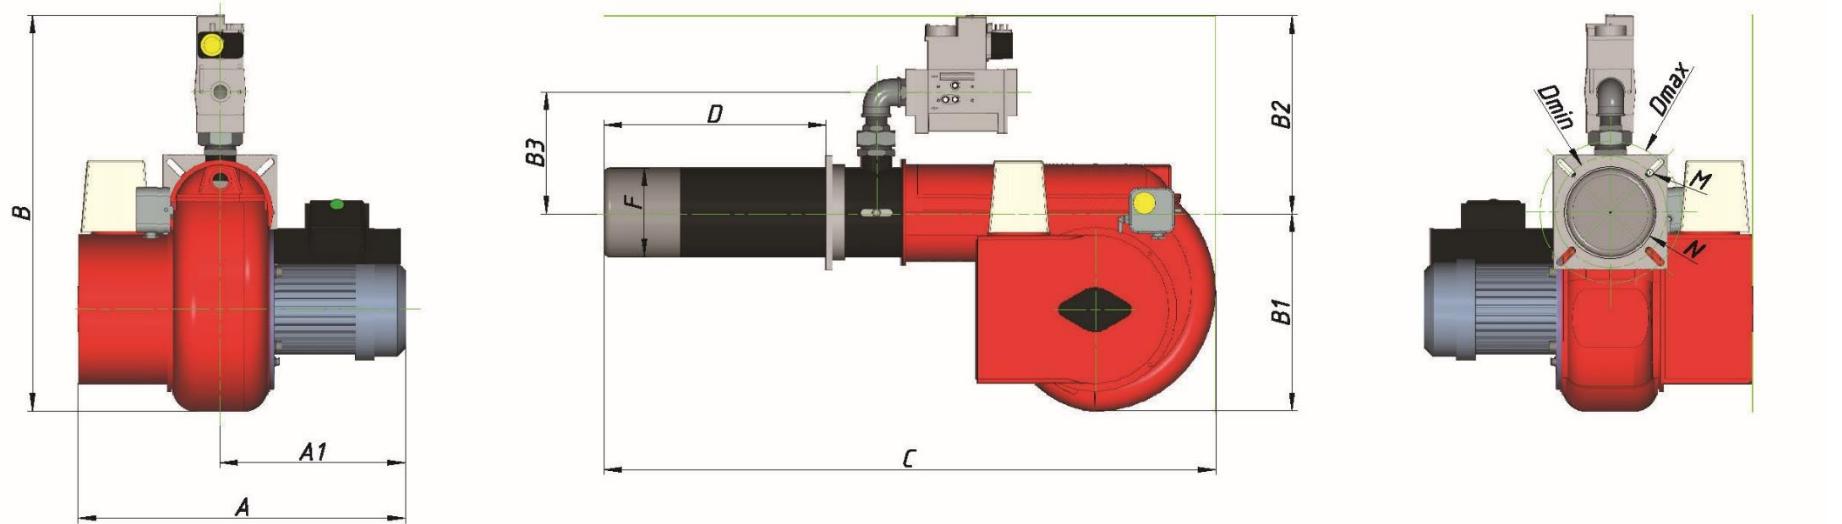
Габаритные и присоединительные размеры горелок ГГБ-0,63
